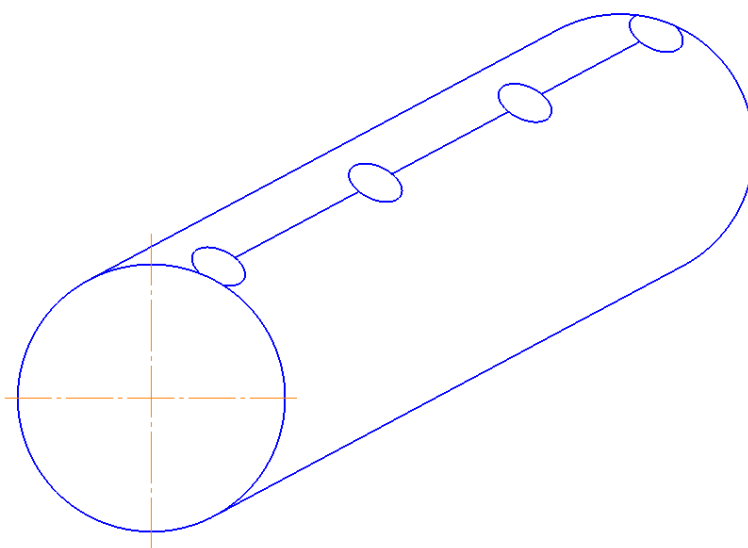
Эскиз операции сборки с прихваткой
